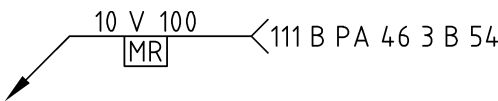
Symbolhaftes Bezeichnungsbeispiel einer Schweißnaht nach DIN EN 22553
